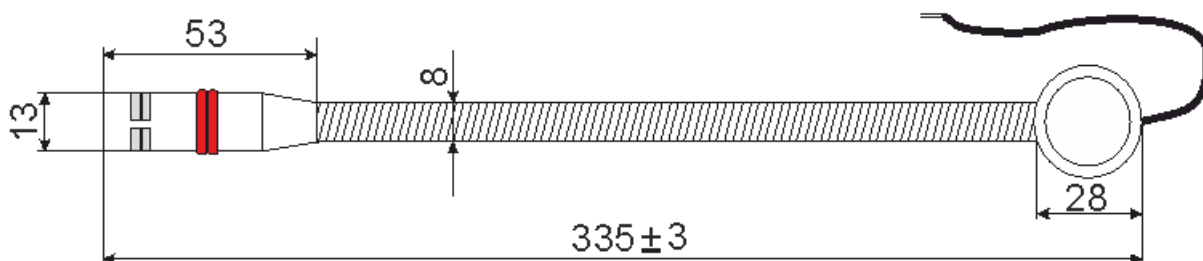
Внешний вид и габаритные размеры основного микрофона G14-1
